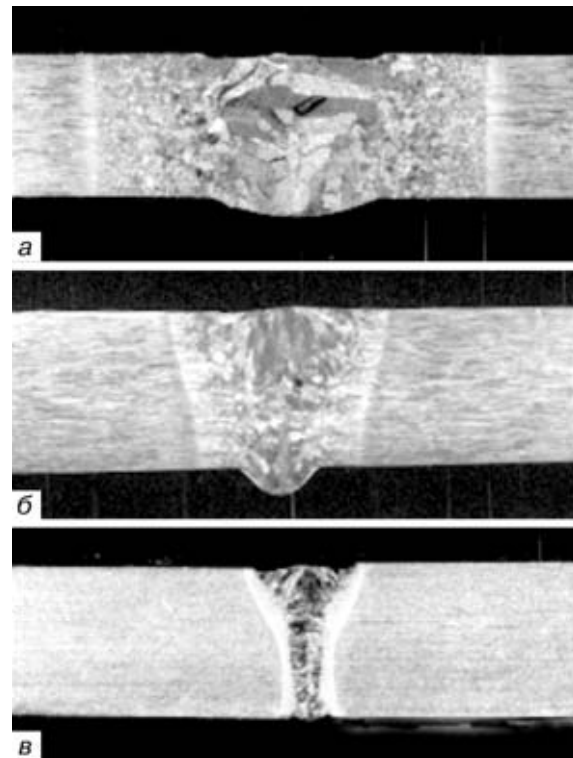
Макроструктура сварных соединений: а — дуговая; б — электронно-лучевая; в — лазерная сварка
